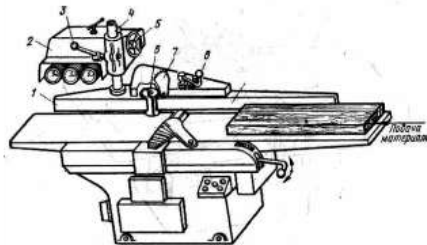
Двусторонний фуговальный станок с горизонтальным и вертикальным шпинделями С2Ф3-3
